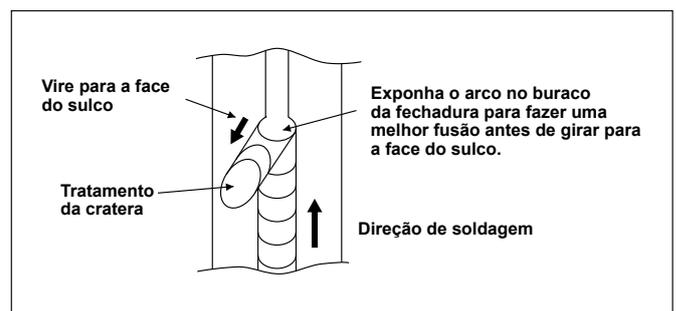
Como terminar a cratera de soldadura para evitar que a cratera fique rachada.
